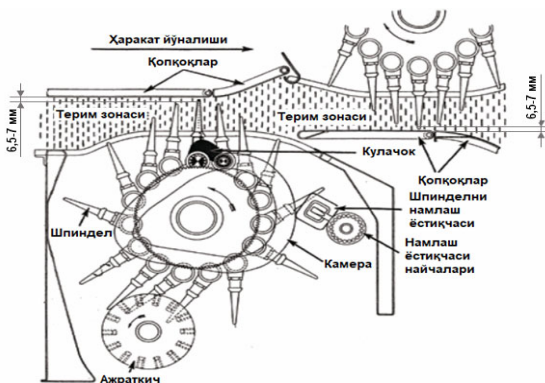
Регулировка рабочий щель уборочного аппарата
